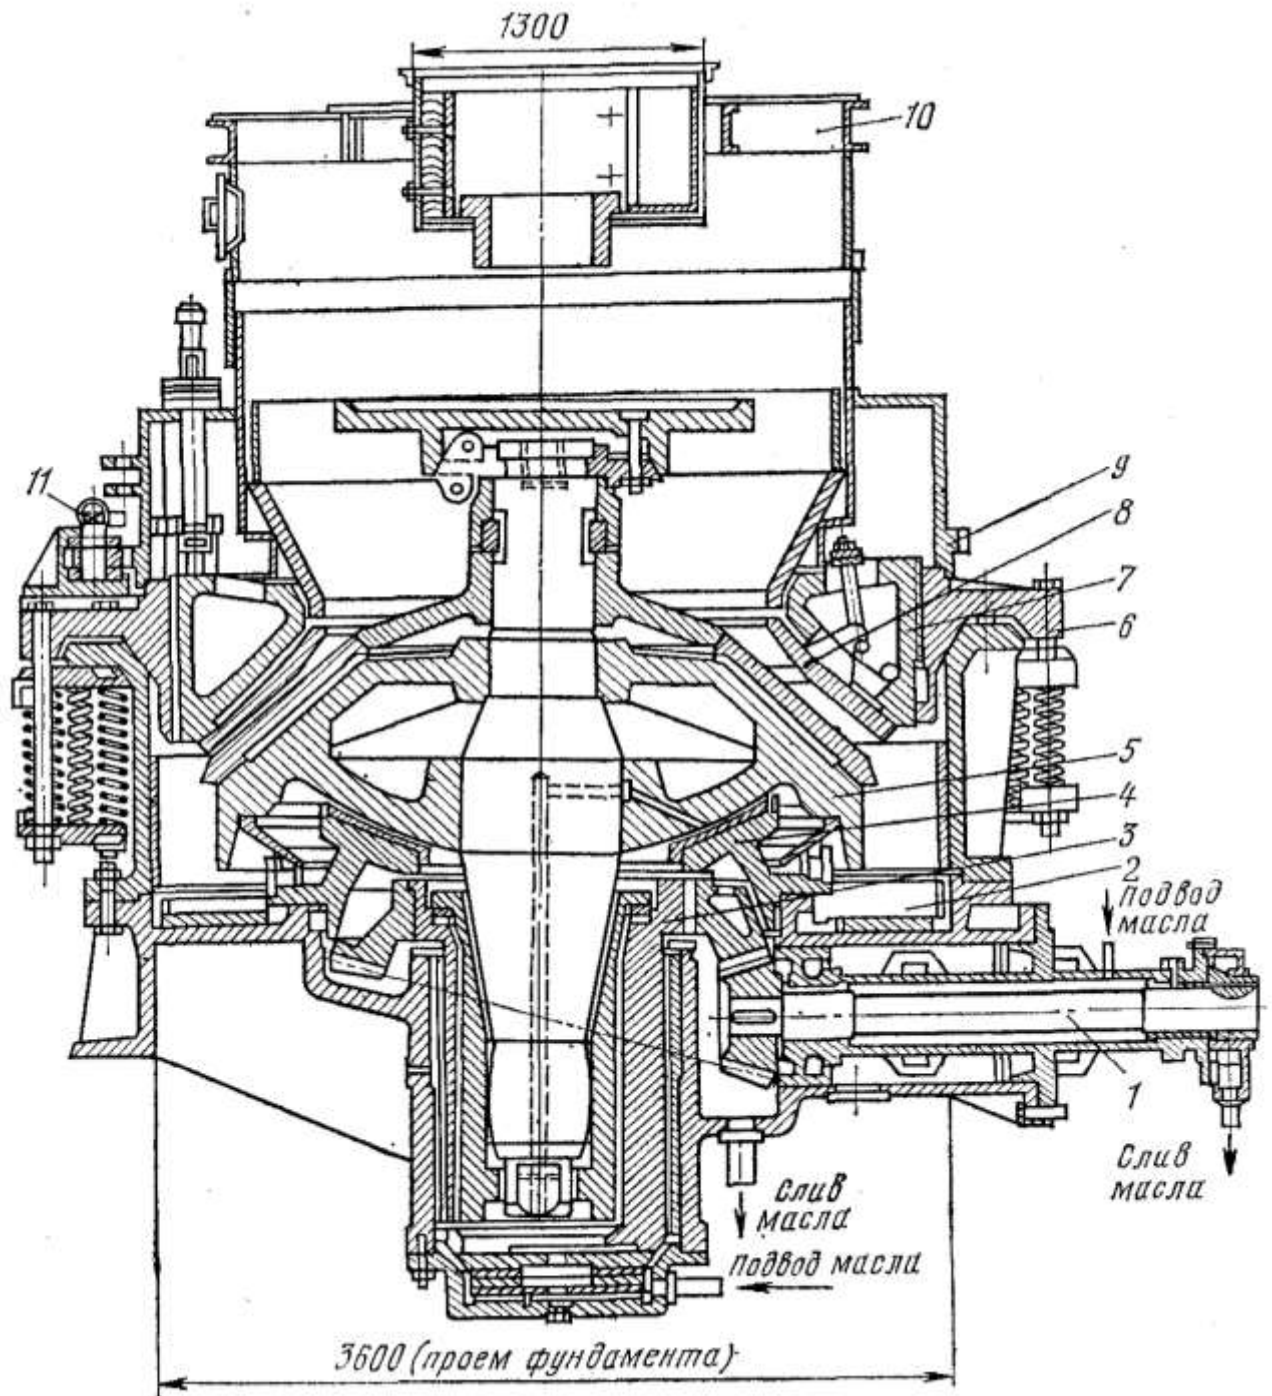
Дробарка м'якого дроблення КМД-3000Т [5-8, 15-18]: 1 – вал приводний; 2 – станина; 3 – стакан ексцентриковий; 4 – чаша опорна; 5 – конус рухомий; 6 – амортизатори; 7 – кільце регулююче; 8 – конус нерухомий; 9 – кожух; 10 – пристрій завантажувальний; 11 – механізм повороту
